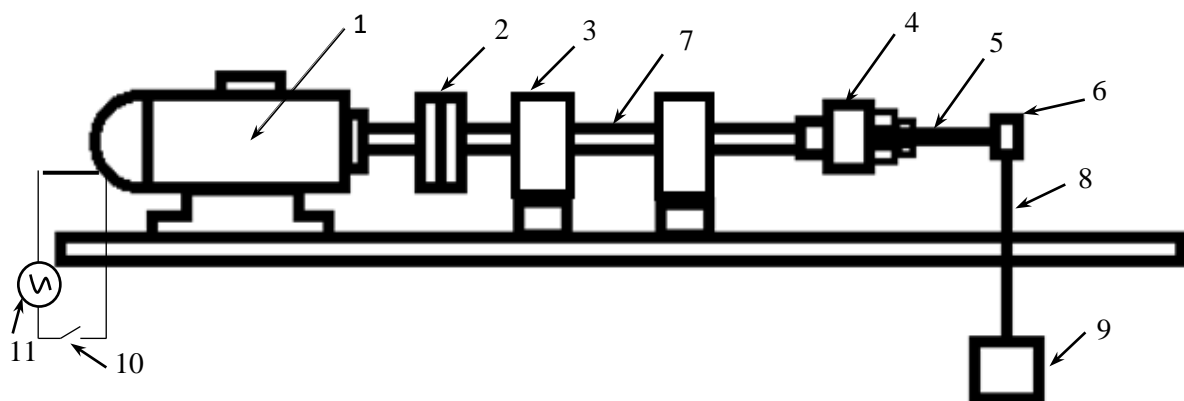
Skema Instalasi Mesin *Continuous Drive Friction Welding
